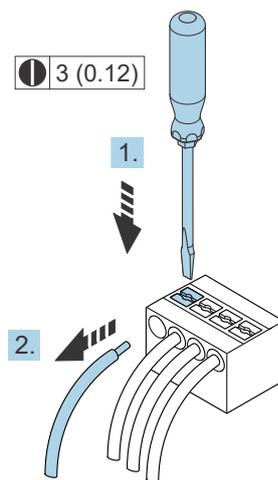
Kabel entfernen. Maßeinheit: mm (in)
